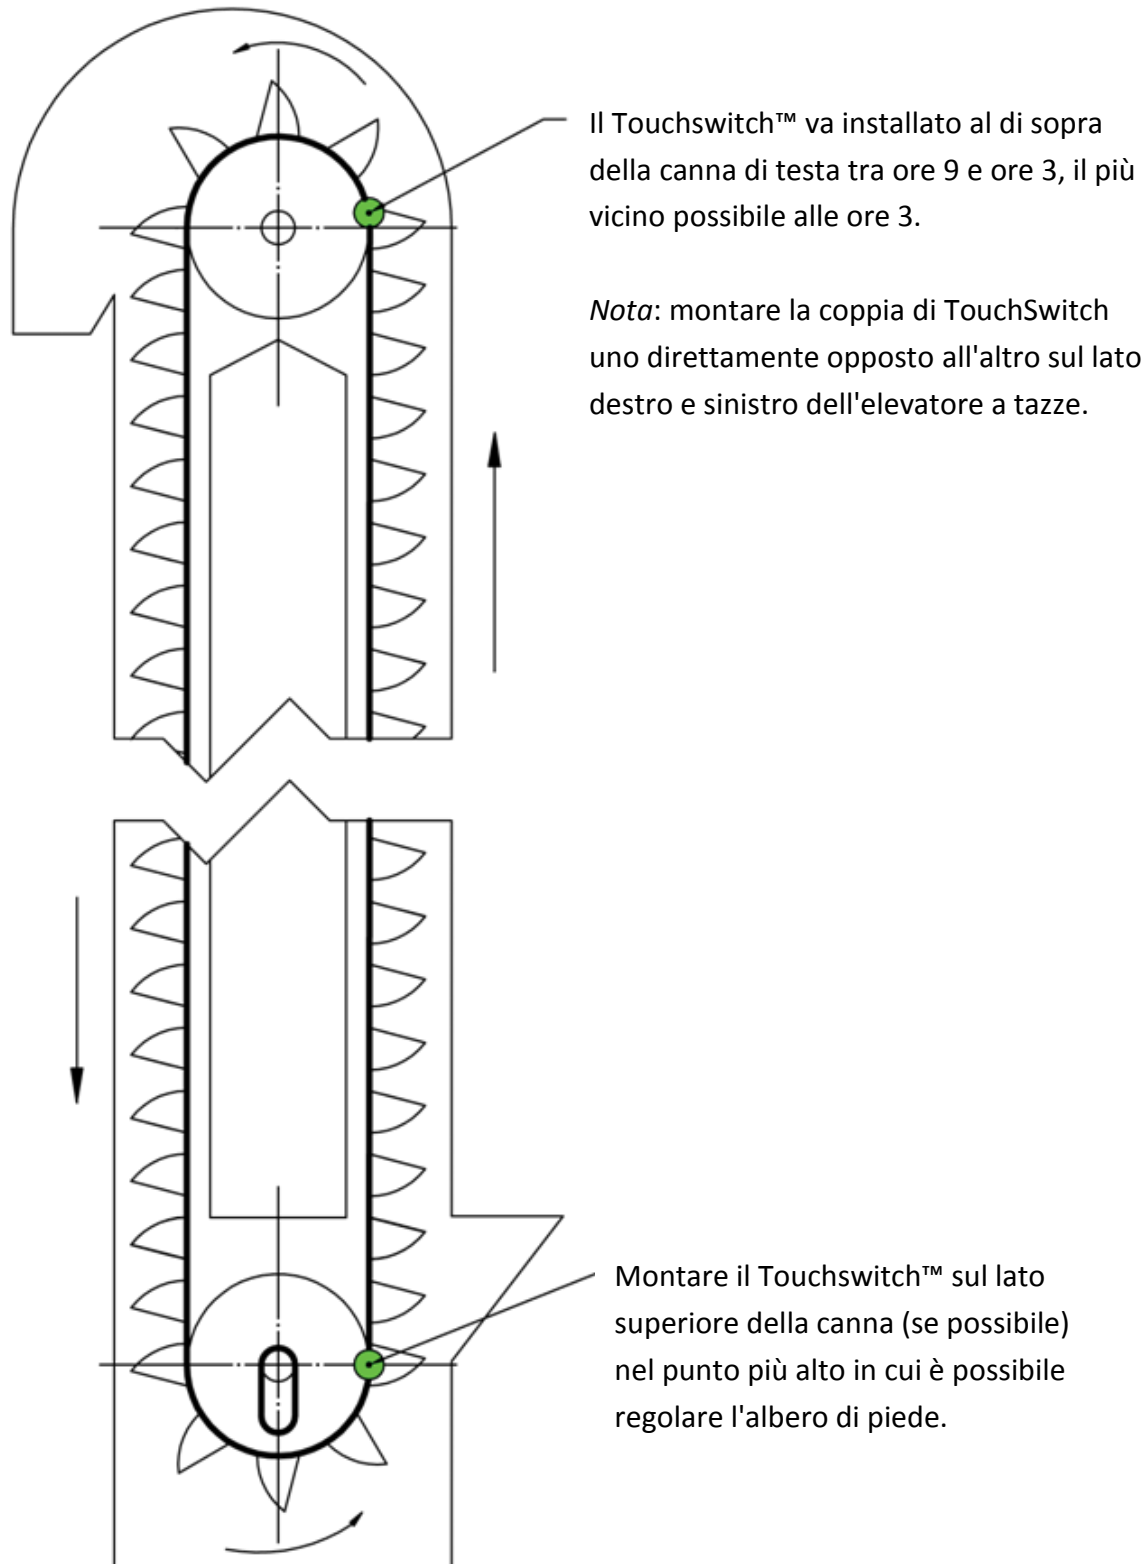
Posizione di montaggio del Touchswitch – Canna dell'elevatore
